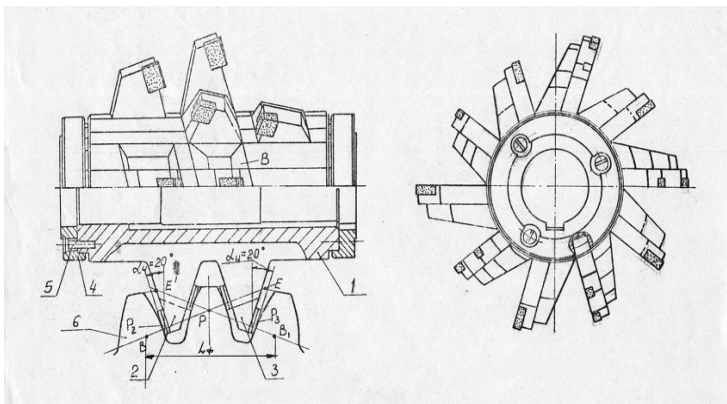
Двухсторонняя однокорпусная фреза со вставными коническими зубчатыми рейками
